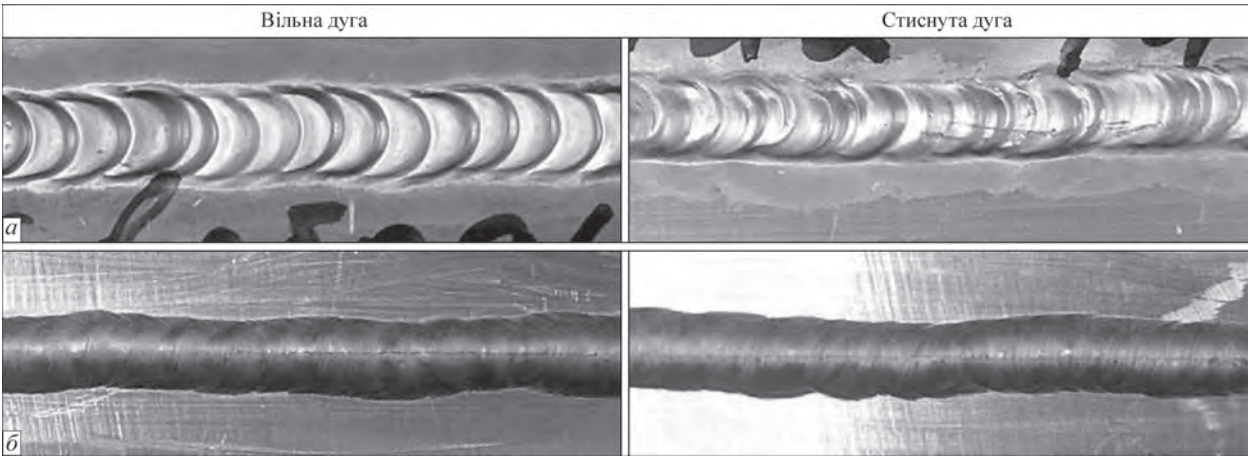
Зовнішній вигляд зварних з’єднань у стані після зварювання: а – лицьова поверхня шва; б – корінь шва
